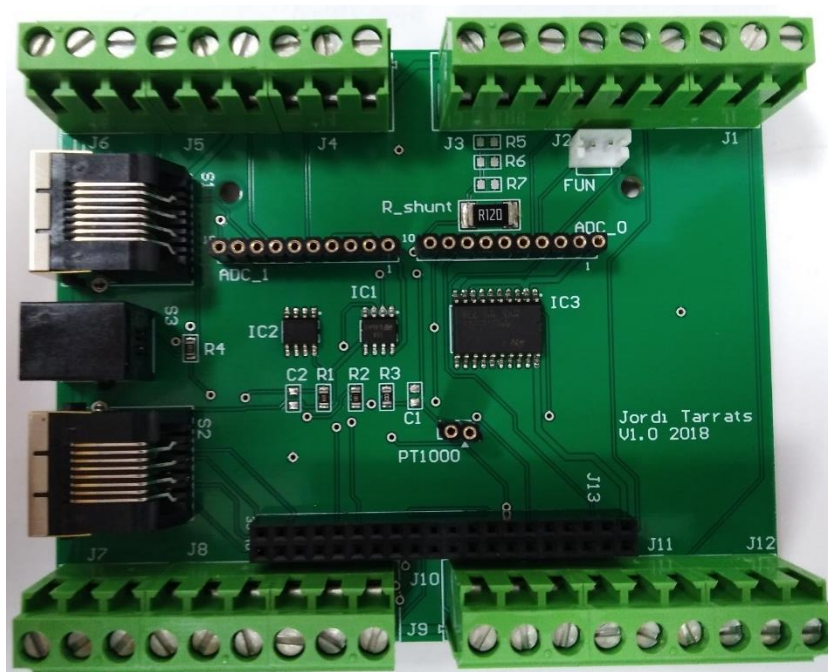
Placa acabada amb tots els components d'SMT i de THT soldats.
